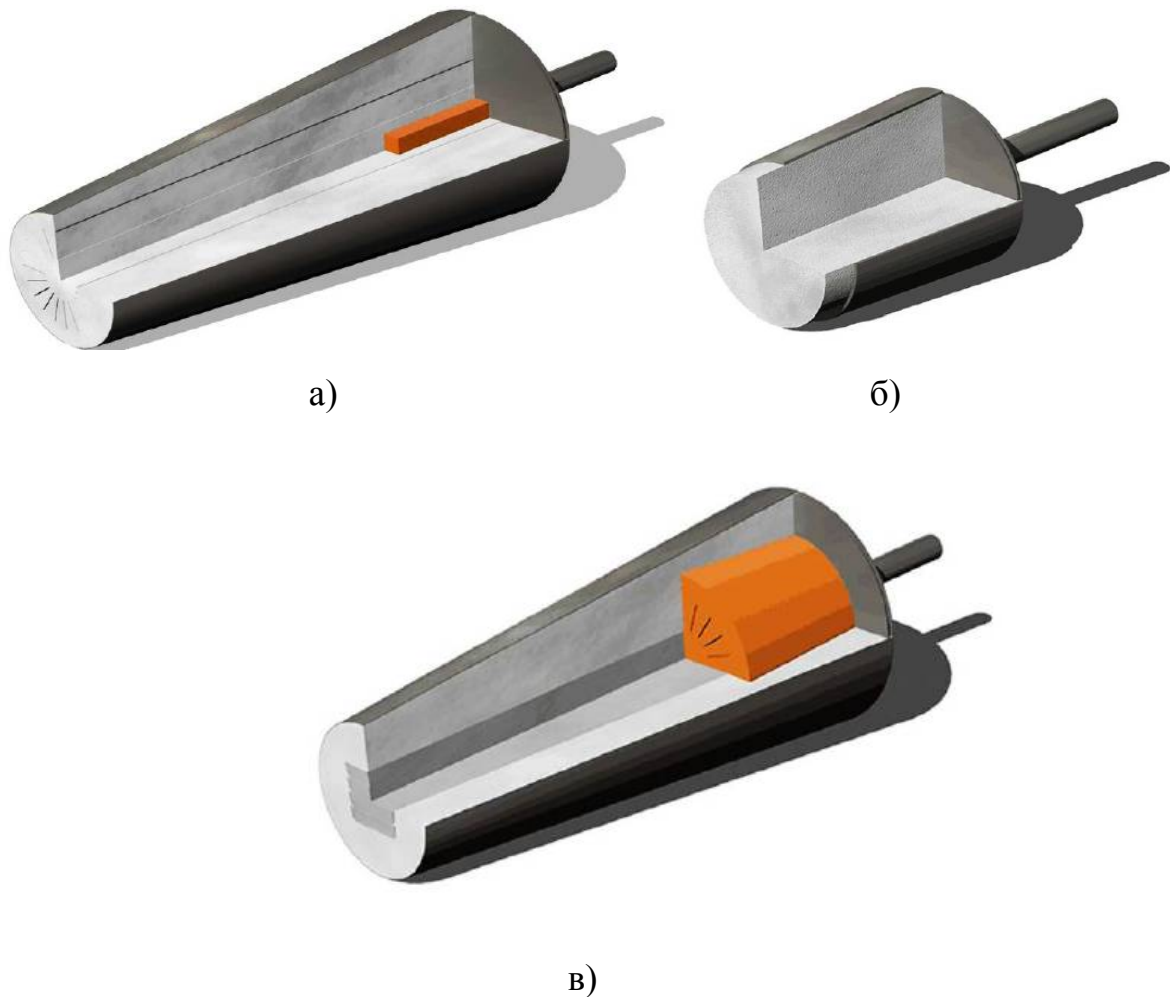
Сучасні конструкції донних продувальних блоків для сталерозливних ковшів [4]: а – щілинний тип; б – пористий тип; в – пластинчатий тип
